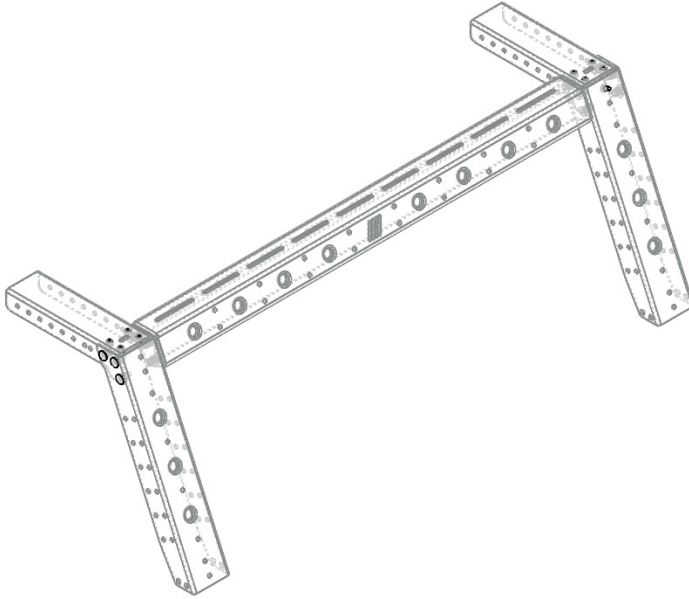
komplett verschraubte Eckstrebe / completely bolted corner strut
